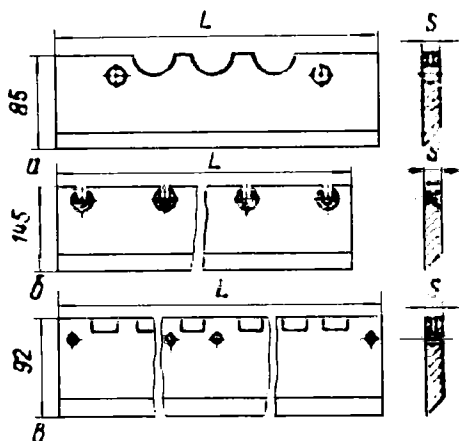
Рубильные ножи с регулировкой установочной ширины:
